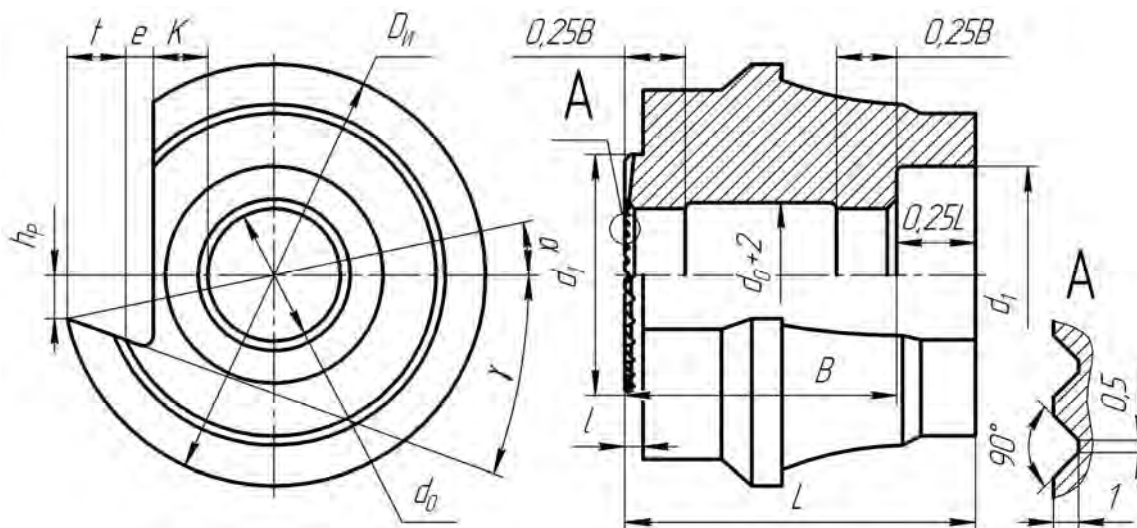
Габаритные и присоединительные размеры фасонных резцов
